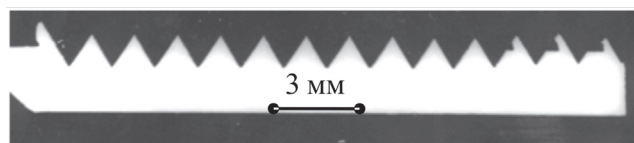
Фотография среза резьбового профиля, полученного ИДР; медь М2, резьба М20×1,5
